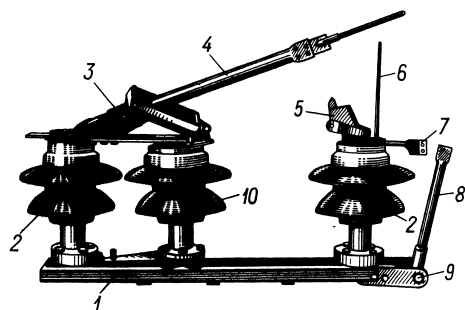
Разъединитель с комбинированным движением ножа для наружной установки (35 кВ, 600 А)
